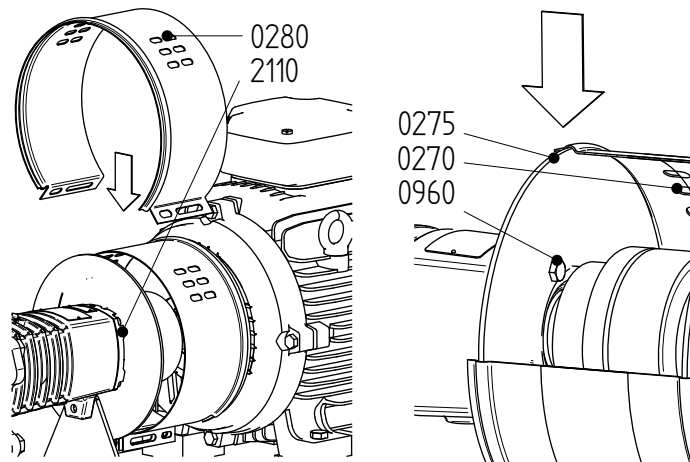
Montieren der Schutzhaube auf der Pumpenseite.
